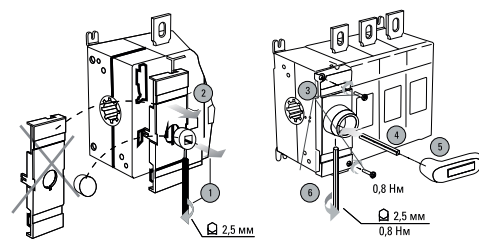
Установка рукоятки управ. прямой установки 160-250А
